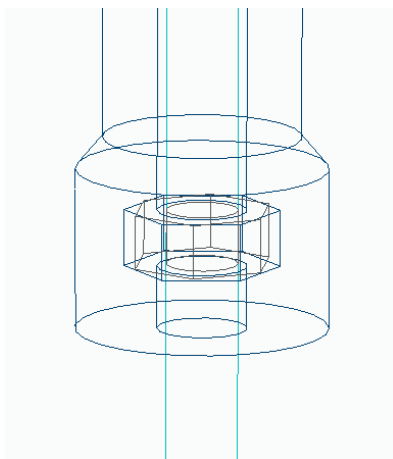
Dibujo de la tuerca dentro del pistón
